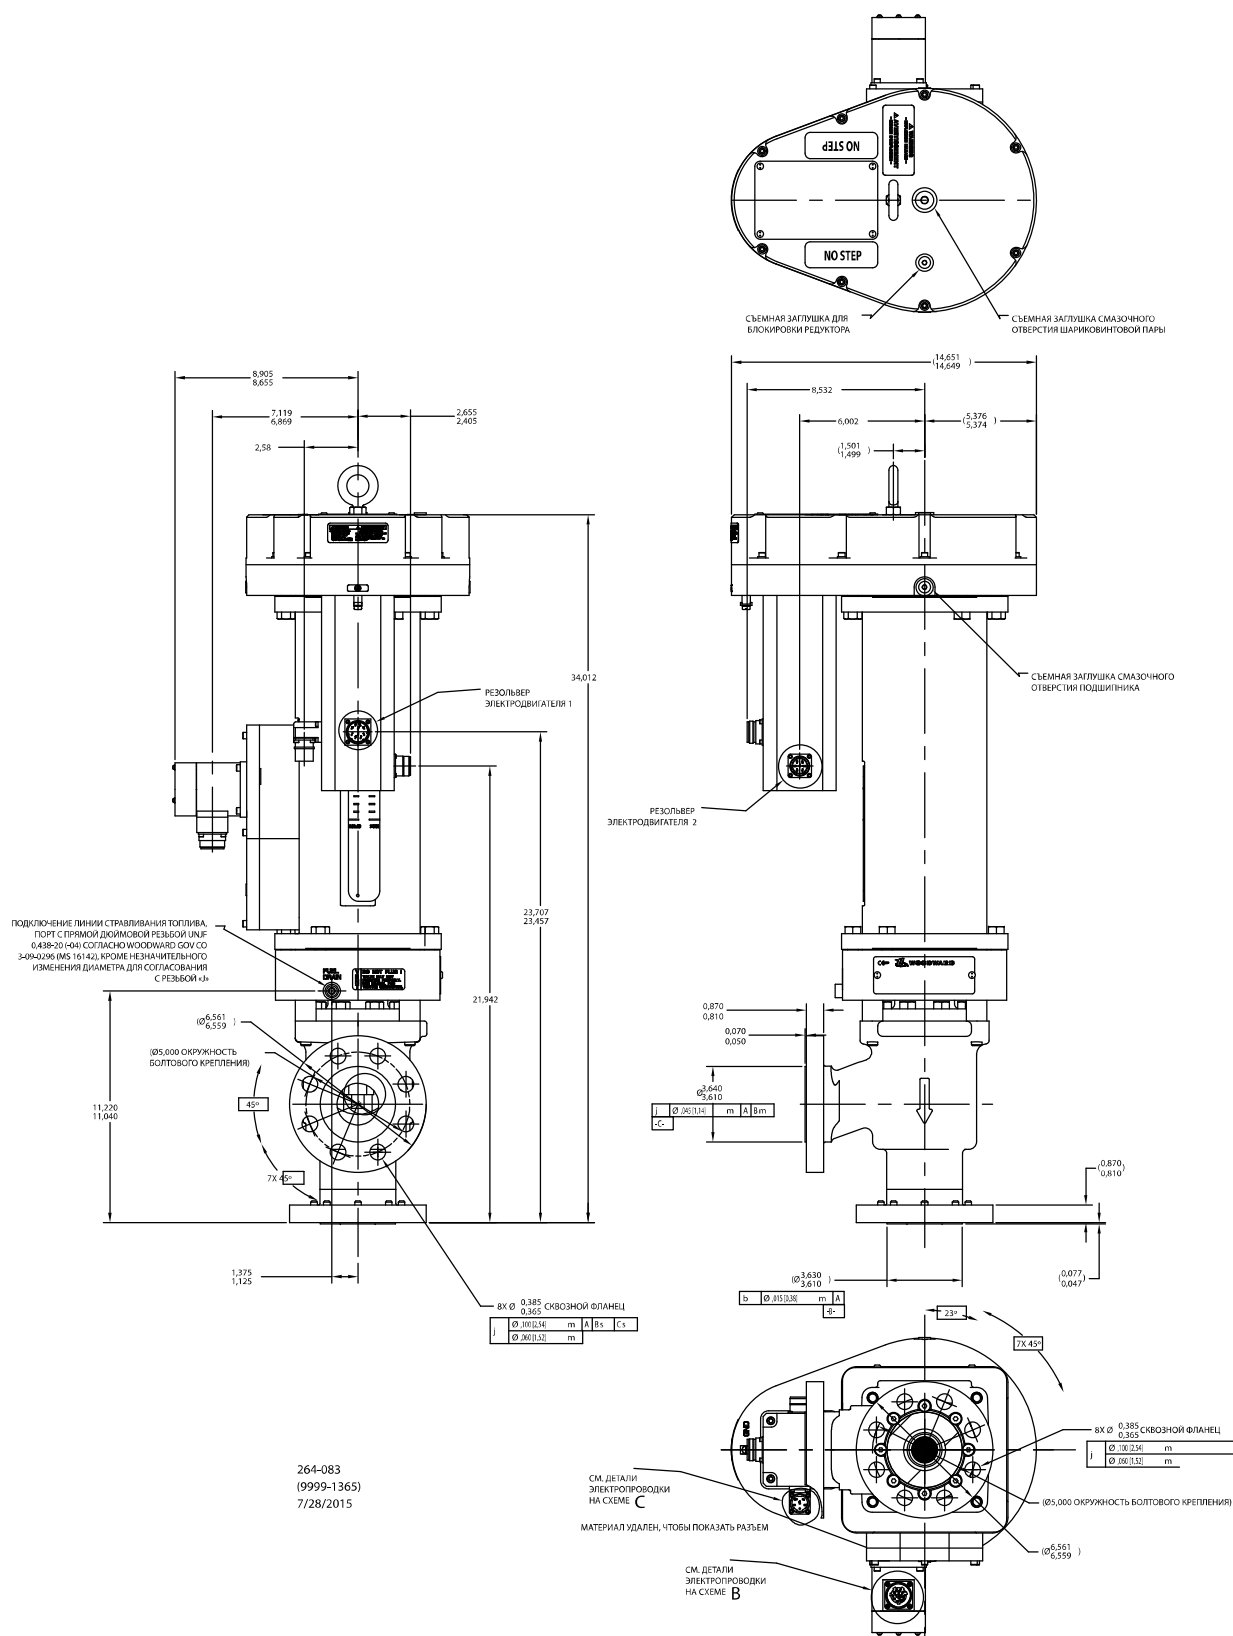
а. Габаритный чертеж (2-дюймовый клапан LESV класса 300)
